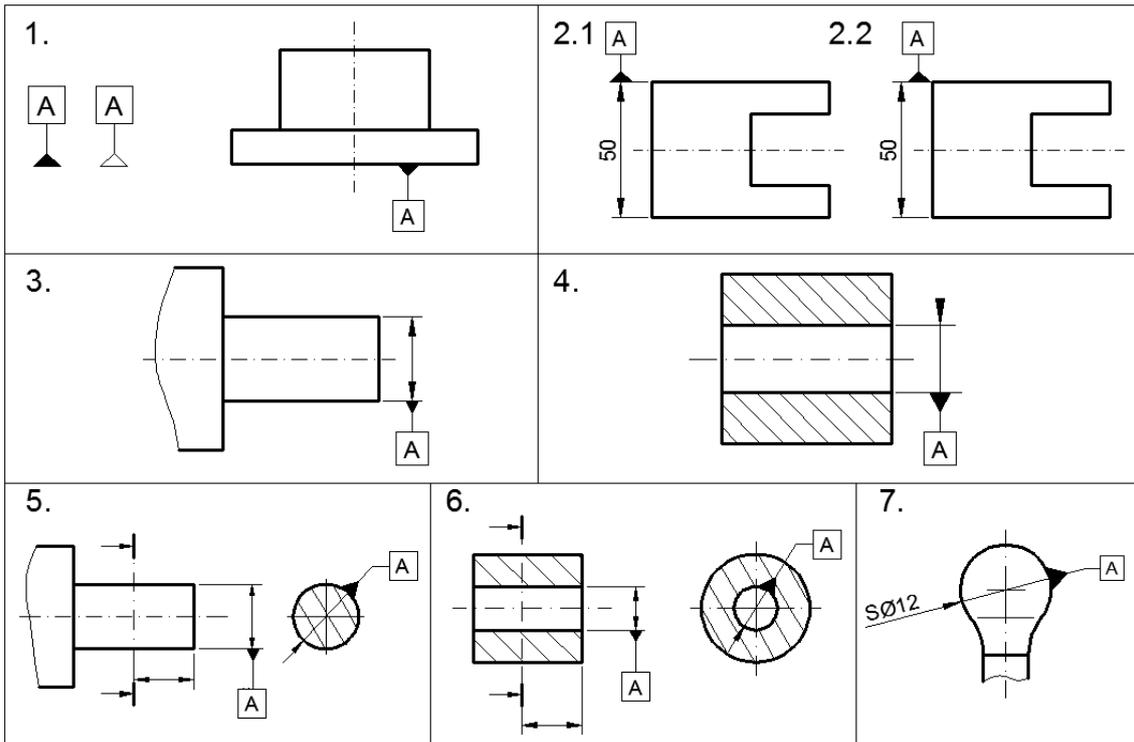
Acotación de la referencia de tolerancias geométricas.
